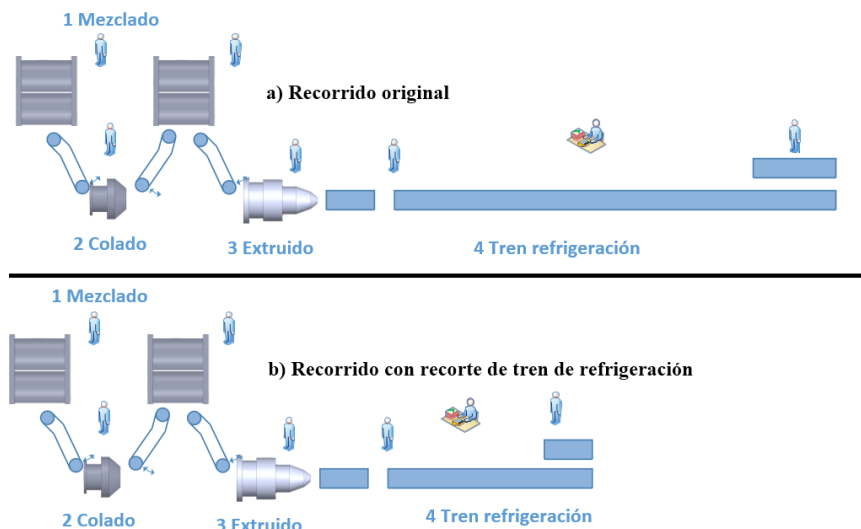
Vista de planta de la zona de trabajo; a) distancia de recorrido original, b) distancia de recorrido con recorte de tren de refrigeración.
